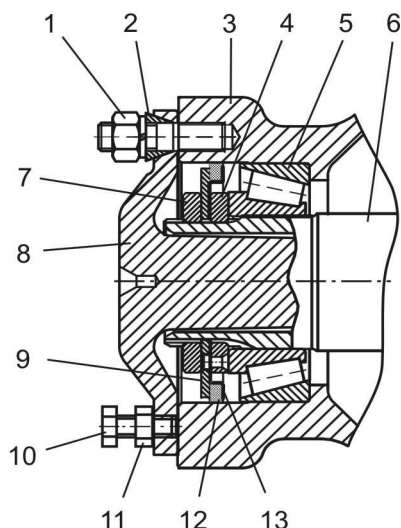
Крепление ступицы заднего колеса (ПАЗ-4234)
